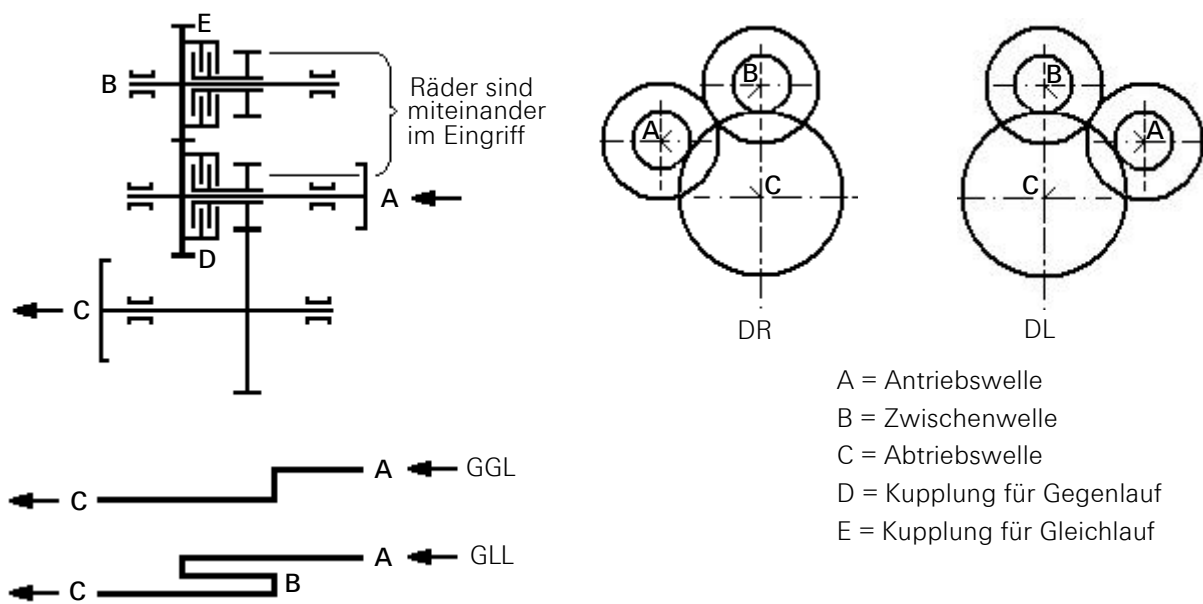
Kraftflussschema der D-Ausführung (Beispiel, GLL = Gleichlauf, GGL = Gegenlauf)
